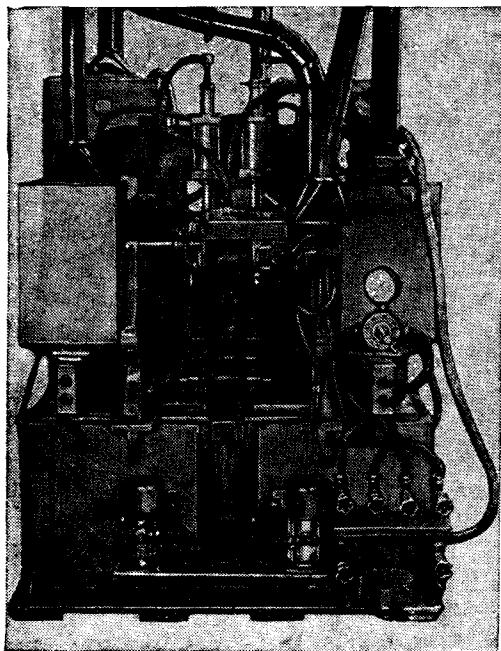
Сварочный автомат АТПА2Х30-2
